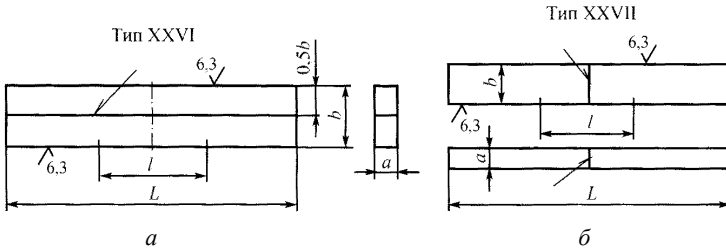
Сварные соединения. Плоские образцы типов XXVI (а) и XXVII (б) для испытания на изгиб:  $L$  – общая длина образца, мм;  $l$  – длина рабочей части образца, мм;  $a$  – толщина образца, мм;  $b$  – ширина образца, мм (стрелками обозначены сварные швы)
